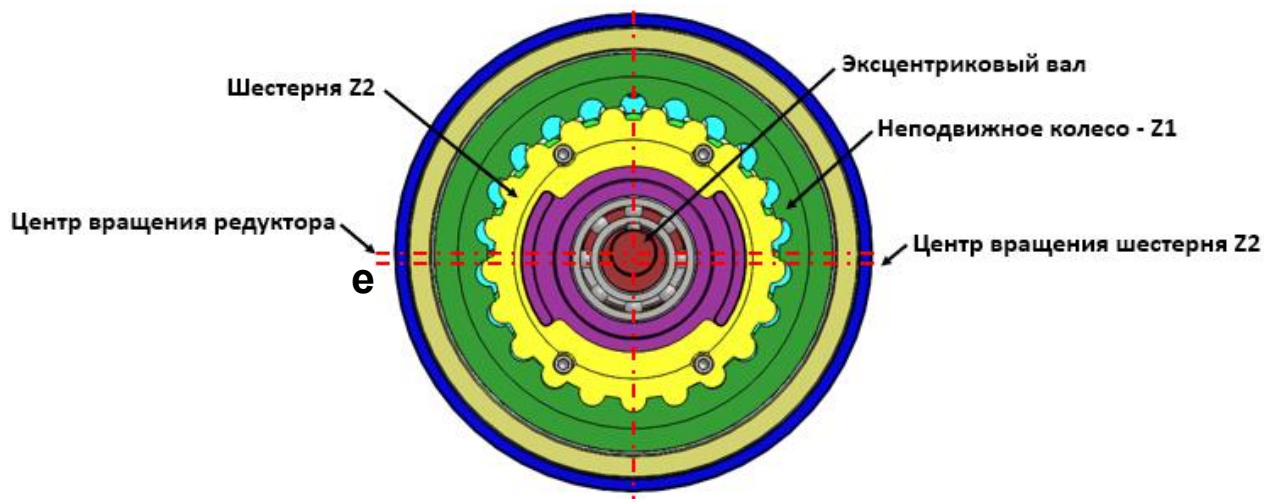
Центр вращения эксцентрикового вала и шестерни Z2 “e”.
